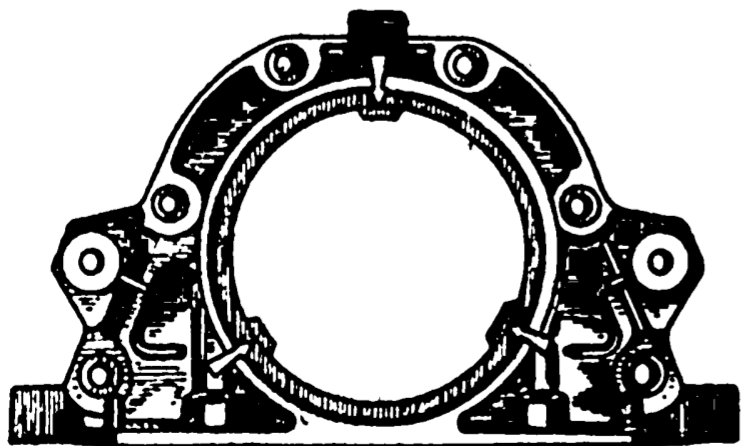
Держатель заднего сальника коленчатого вала. Стрелками указаны выступы для центрирования держателя относительно фланца коленчатого вала
